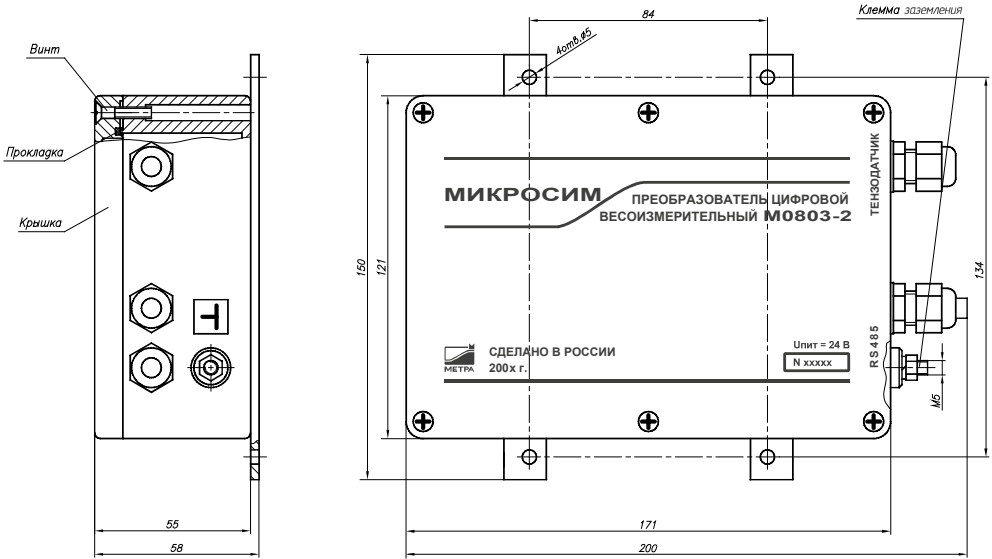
Внешний вид, габаритные и присоединительные размеры преобразователя
